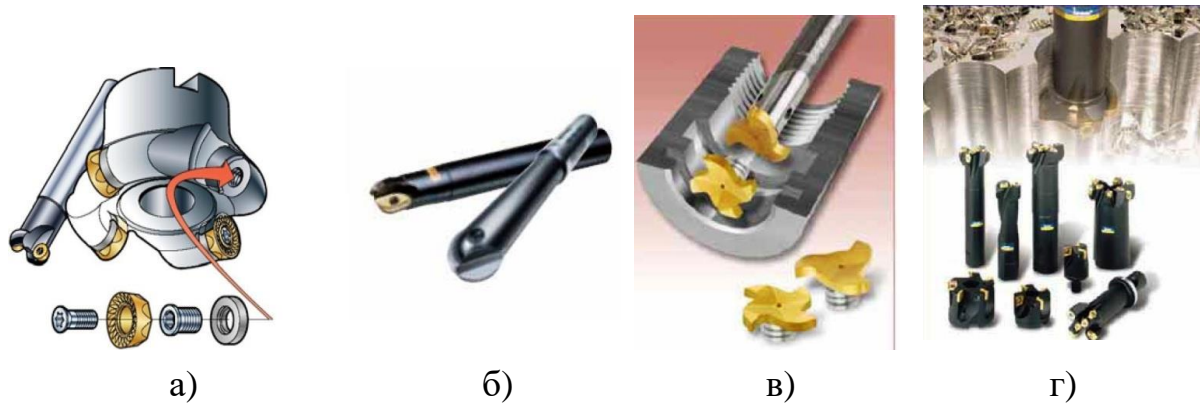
Фрези CoroMill200 (а); CoroMillR216 і CoroMillR216F (б); закріплення інструментів невеликих діаметрів (в); плунжерні фрези (г)
